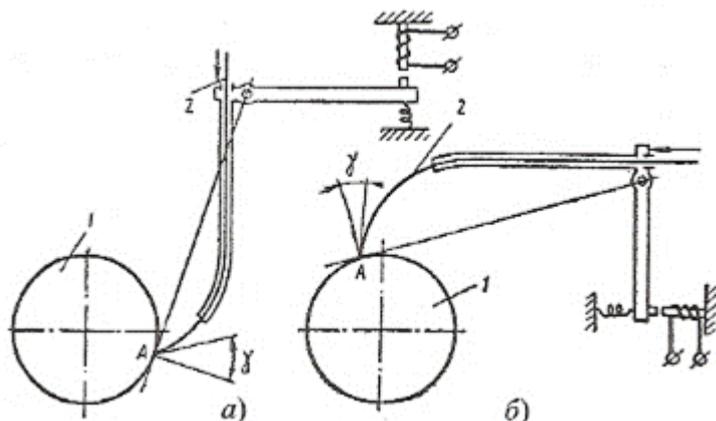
Схема бокового (а) и верхнего (б) подвода проволоки к детали: 1 — деталь, 2 — электрод
